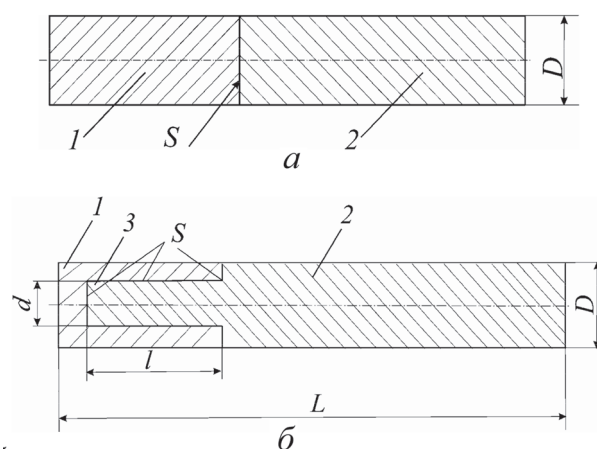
Эскизы биметаллических заготовок, получаемых различными методами: а – биметаллическая заготовка, полученная методами сварки трением, электроконтактной сварки, пайки; б – биметаллическая заготовка, полученная методом горячего выдавливания; 1 – рабочая часть; 2 – хвостовик; 3 – прошивень
